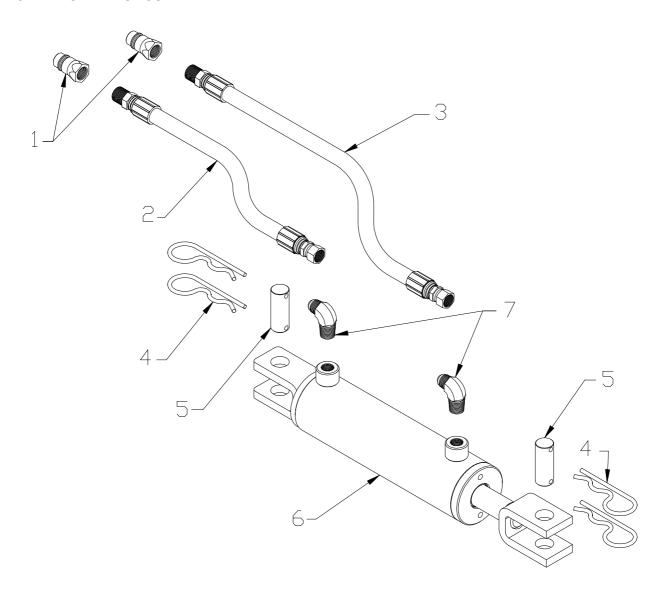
, Ens. del cilindro hidráulico No. CH3080 y Líneas hidráulicas.
